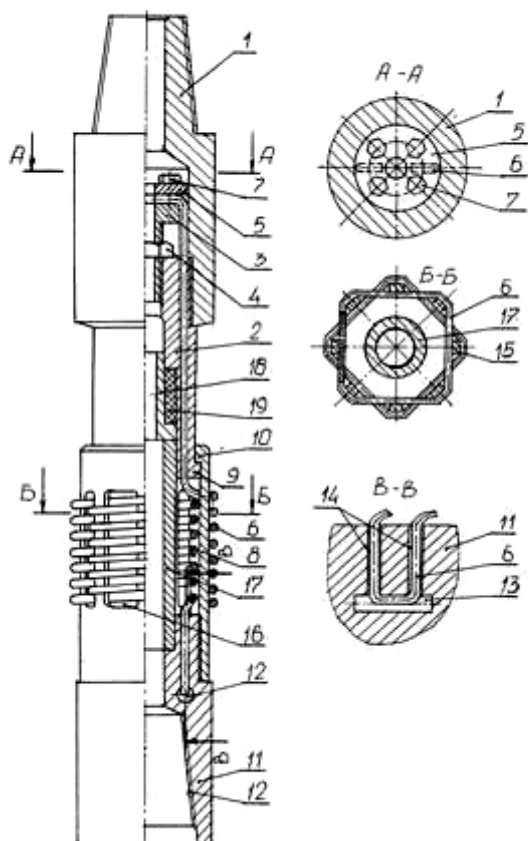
Амортизатор бурильной колонны: 1, 11 – переходник соответственно верхний и нижний; 2 – корпус; 3, 7 – винты; 4 – гайка; 5 – диск; 6 – канат; 8 – каркас; 9, 10 – выступы; 12 – резьба; 13, 14 – каналы; 15 – ребро; 16 – окна; 17 – патрубок; 18, 19 – втулки
